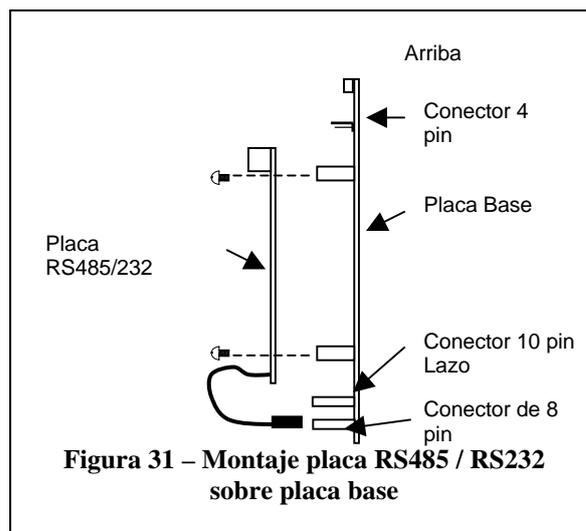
Montaje placa RS485 / RS232 sobre placa base
